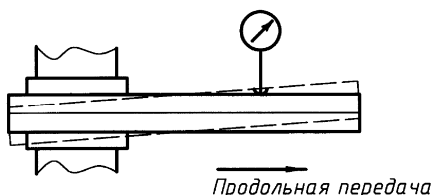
Выверка машинных тисов на столе фрезерного станка
